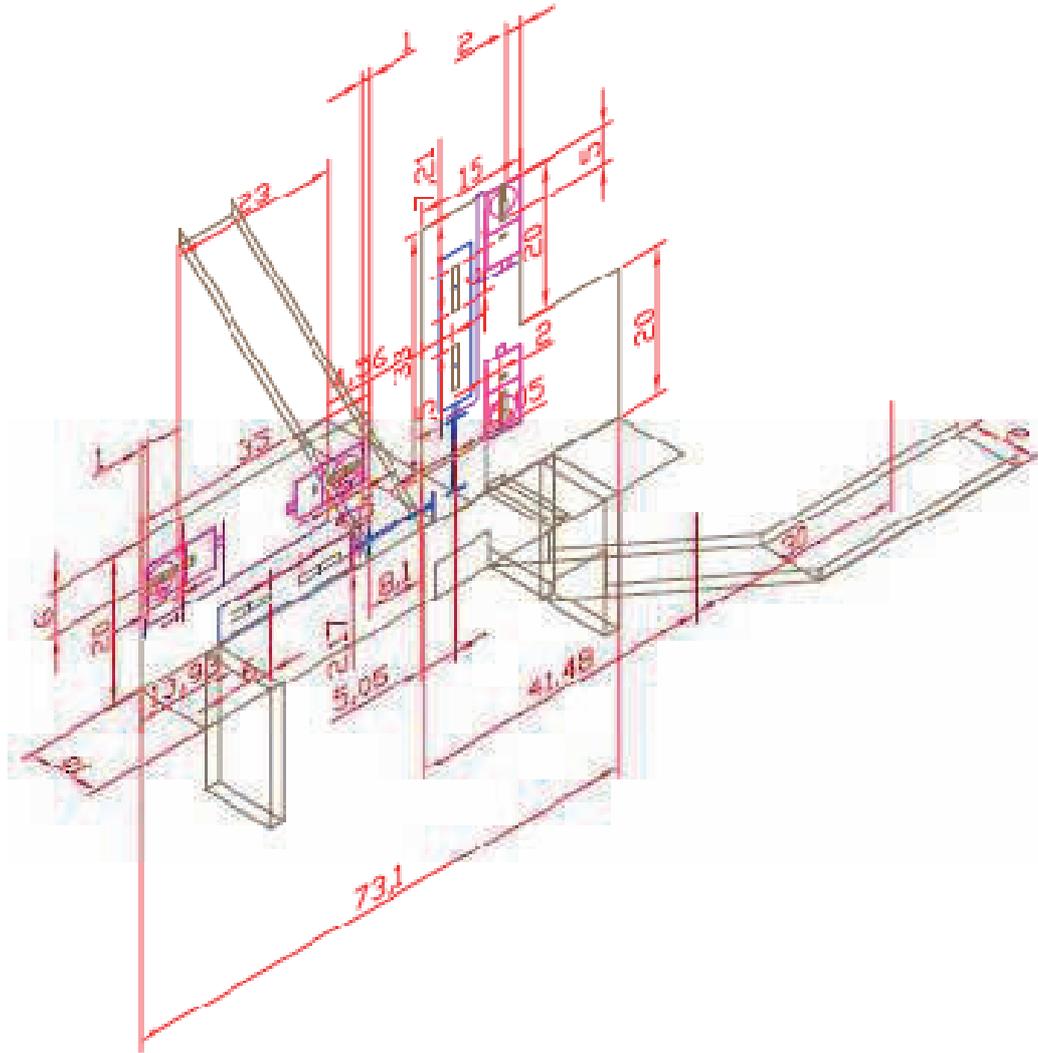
Diseño de máquina (vista lateral 3D)
